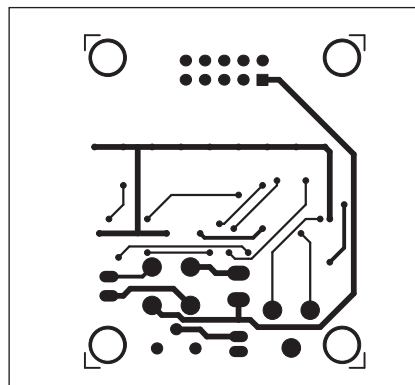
Obrazec desky spojů světelné reklamy (strana TOP)
